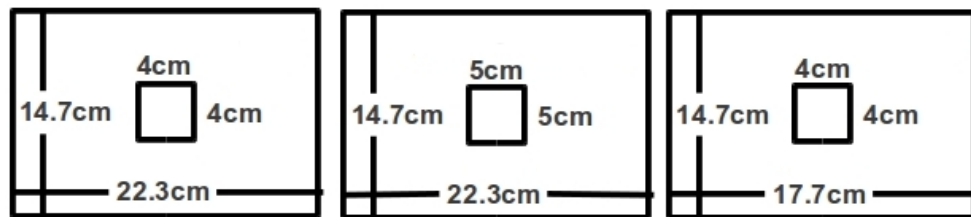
Dimensiones de las paredes donde se ensamblan las placas.
